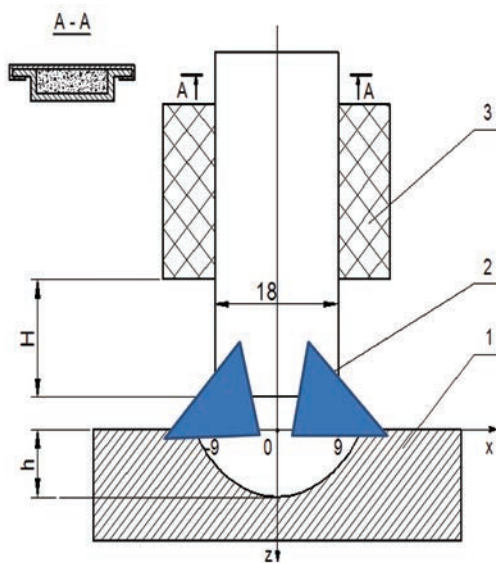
Схема приварки лопаті відцентрового насоса до маточини
